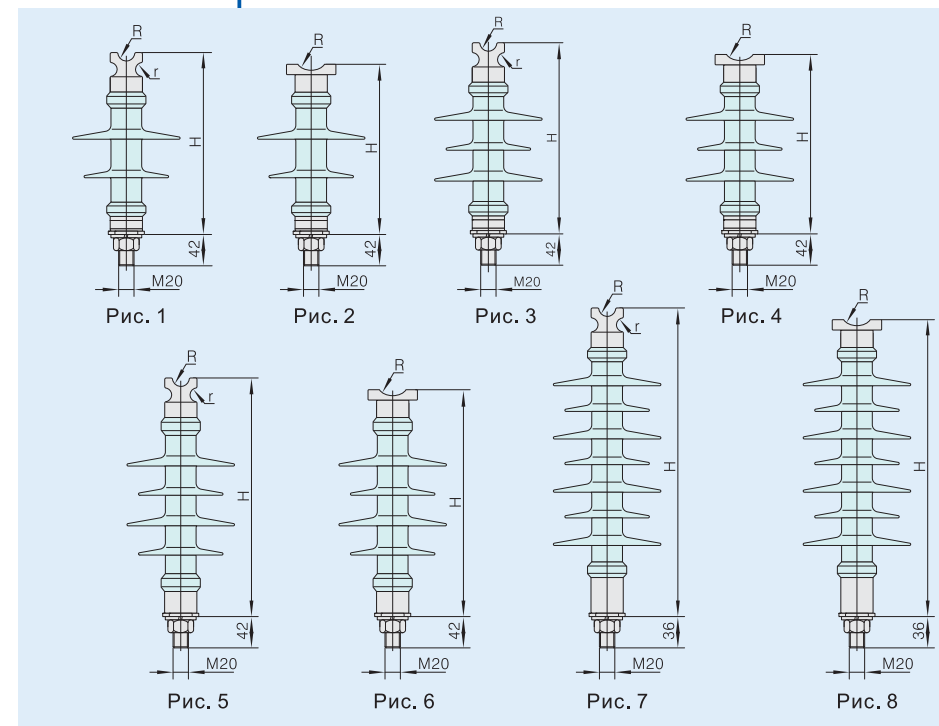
Внешний вид и размеры комбинированных штыревых изоляторов
